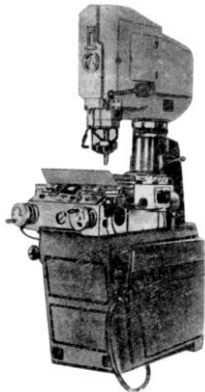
Верстат 4Б722 для обробки штампів і прес-форм.
